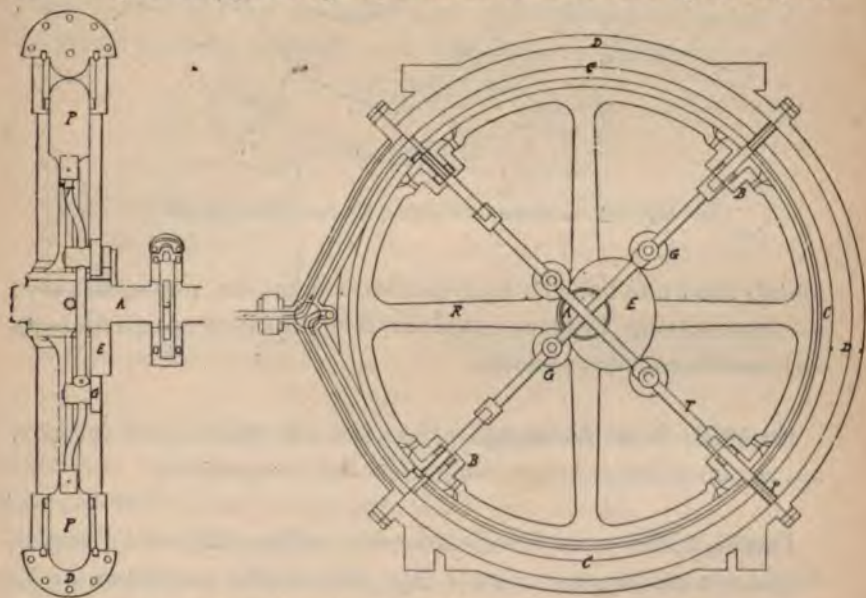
et 121. — Roue à vapeur *Appé* (1865). Coupe transversale. Vue latérale.
